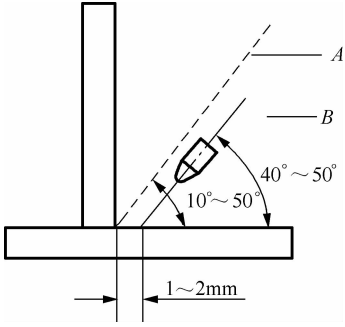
41 T 形接头平角焊时的焊丝位置
